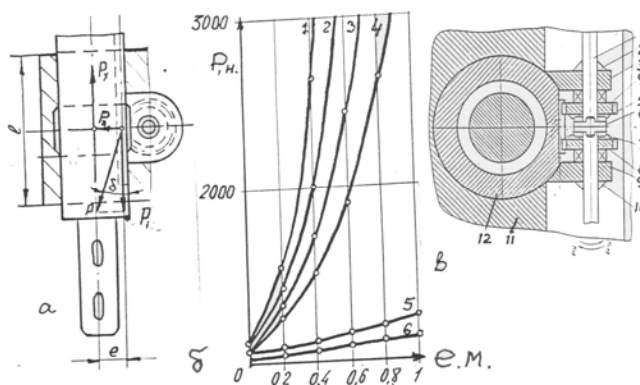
а - конструкція привода подачі вертикально свердильного верстата;
